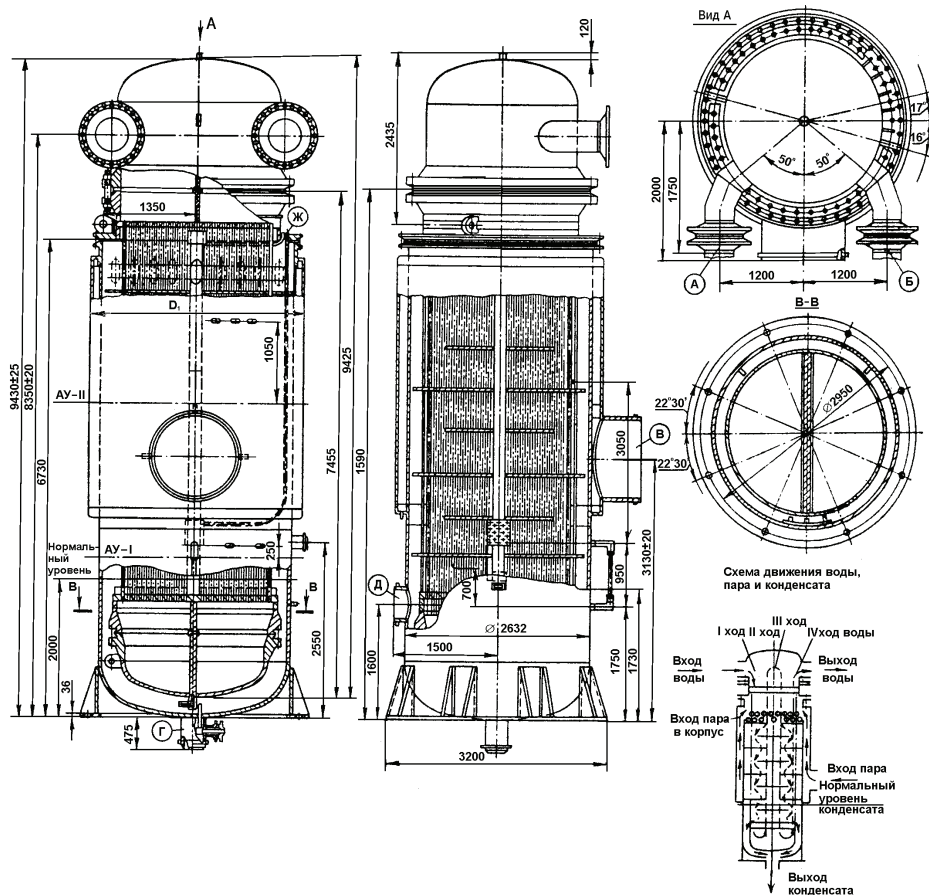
Подогреватель низкого давления ПН-1800-42-8-IA (IIA, IIIA, IVA) [5]:
